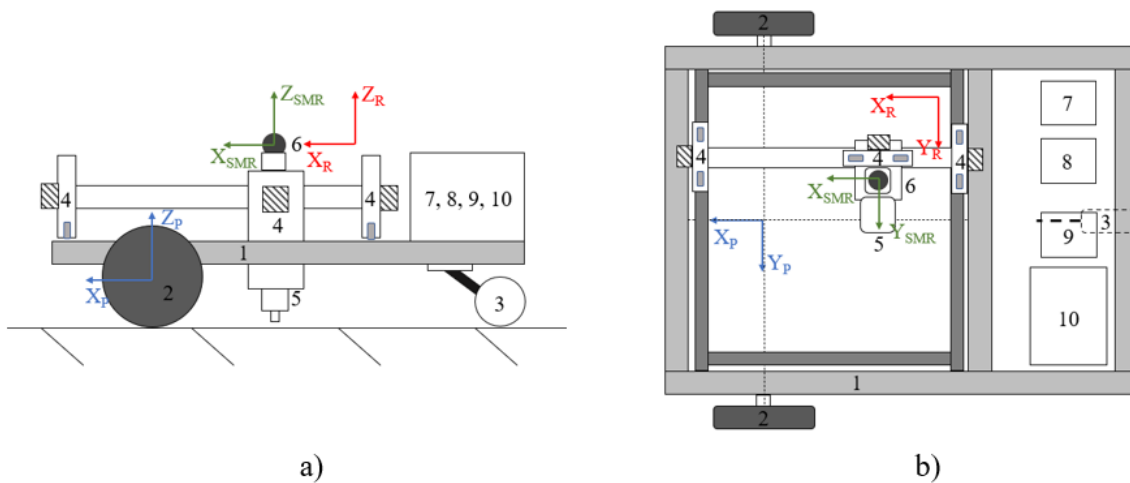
Aufbau des Absteckroboter a) Seitenansicht, b) Draufsicht
